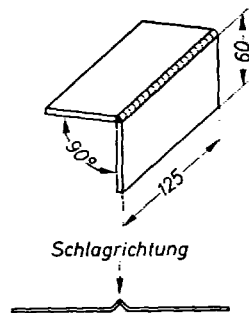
Ecknaht-Prüfstück für Blechschweißer an $s = 1,5$ bis 2 mm
